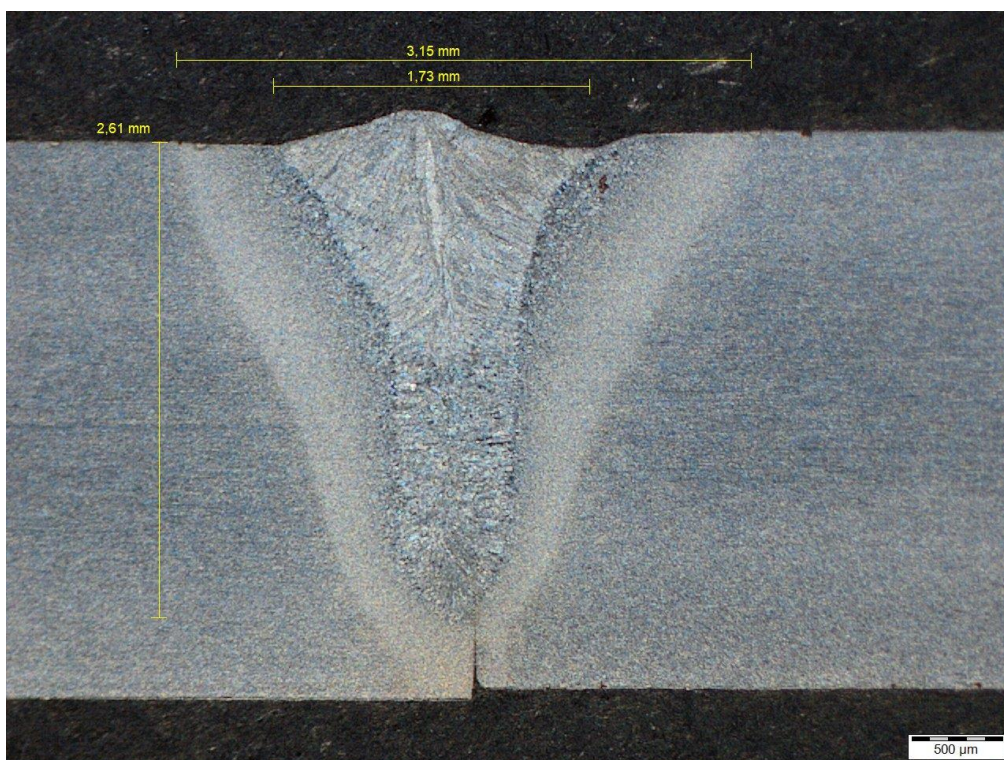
Makrostruktura svaru (laser s přehřevem TIG – vzdálenost elektrody 2 mm)
